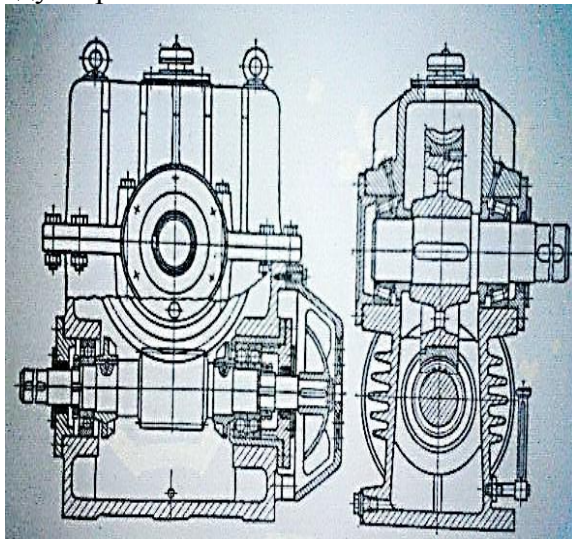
Редуктор черв'ячний одноступінчастий
